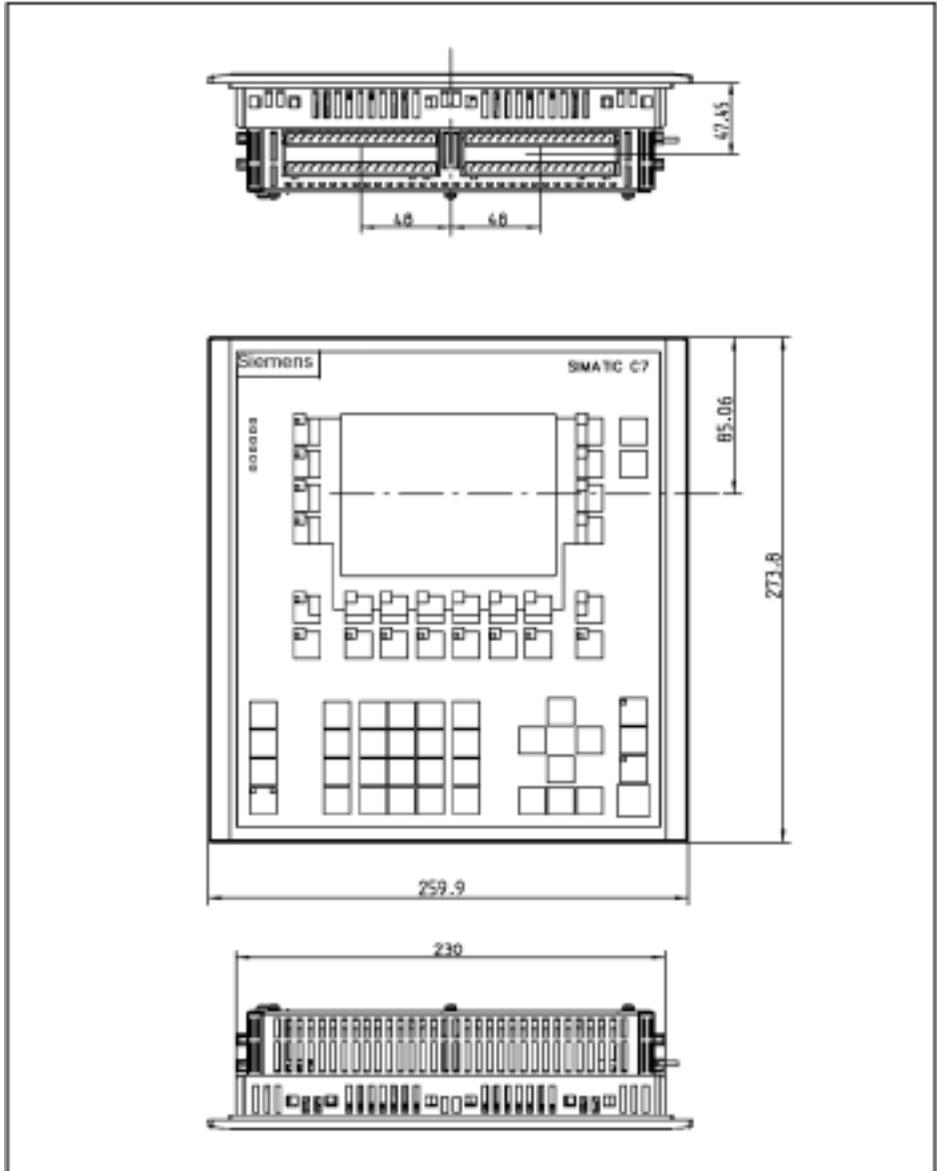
C7-635 Key 的尺寸图(单位 mm)
